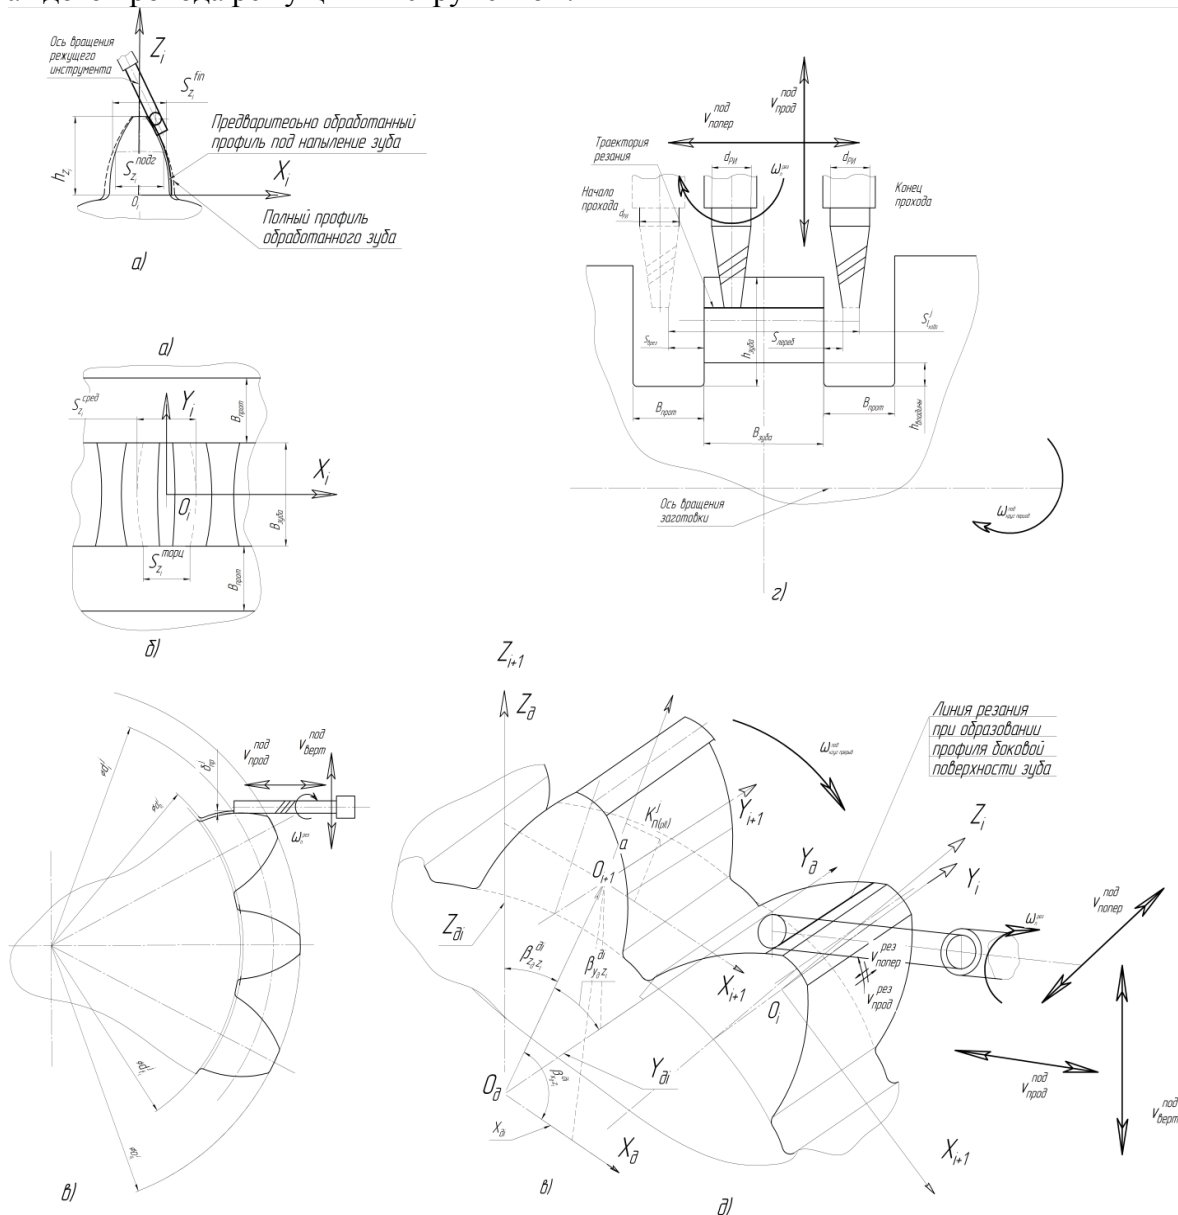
Технологическая схема формообразования профиля зубьев среднего зубчатого венца блок-вала колес: а) форма профиля зуба; б) окончательно сформированный зуб в плане; в) образующая линия режущего инструмента (РИ) срезает припуск; г) поперечный ход РИ при формировании каждой линии на проходе резания; д) аксонометрия заготовки в процессе формообразования профиля зубчатого венца и боковой поверхности зубьев.
